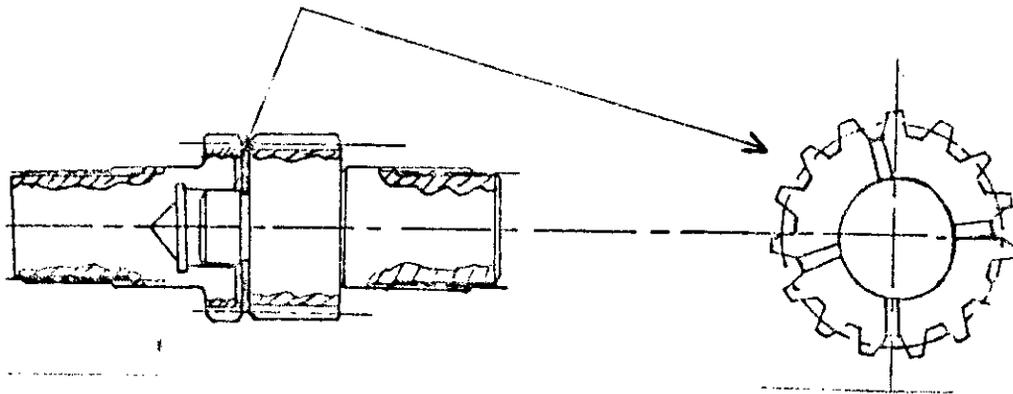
Soudage des surfaces en contact des deux arbres.
